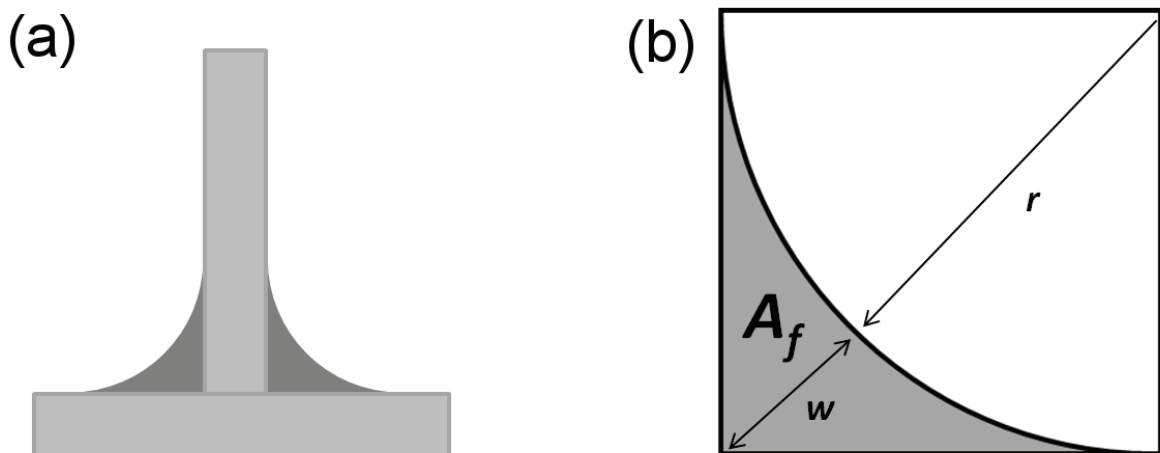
Géométrie de l'éprouvette brasée considérée par Terrill [42] (a) et calcul de l'aire du ménisque formé (b)
